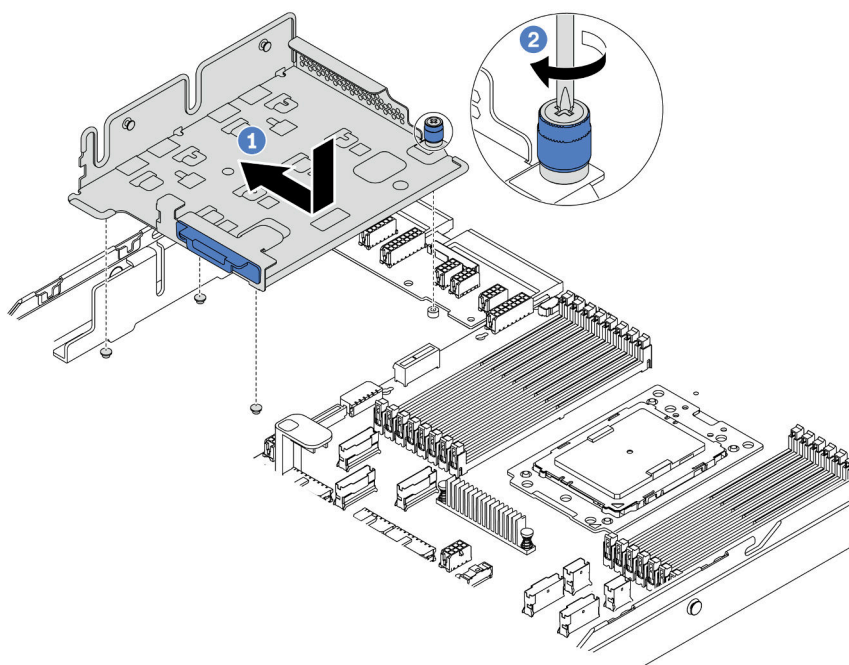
Instalação do suporte de apoio da placa riser/M.2
